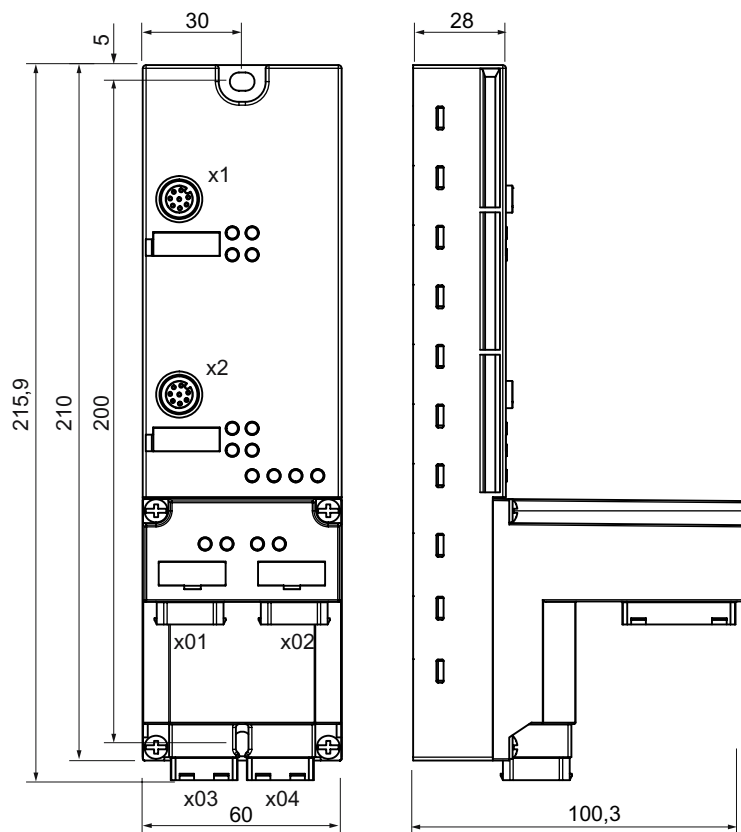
Maßbild eines RF180C mit Busanschlussblock Push Pull
